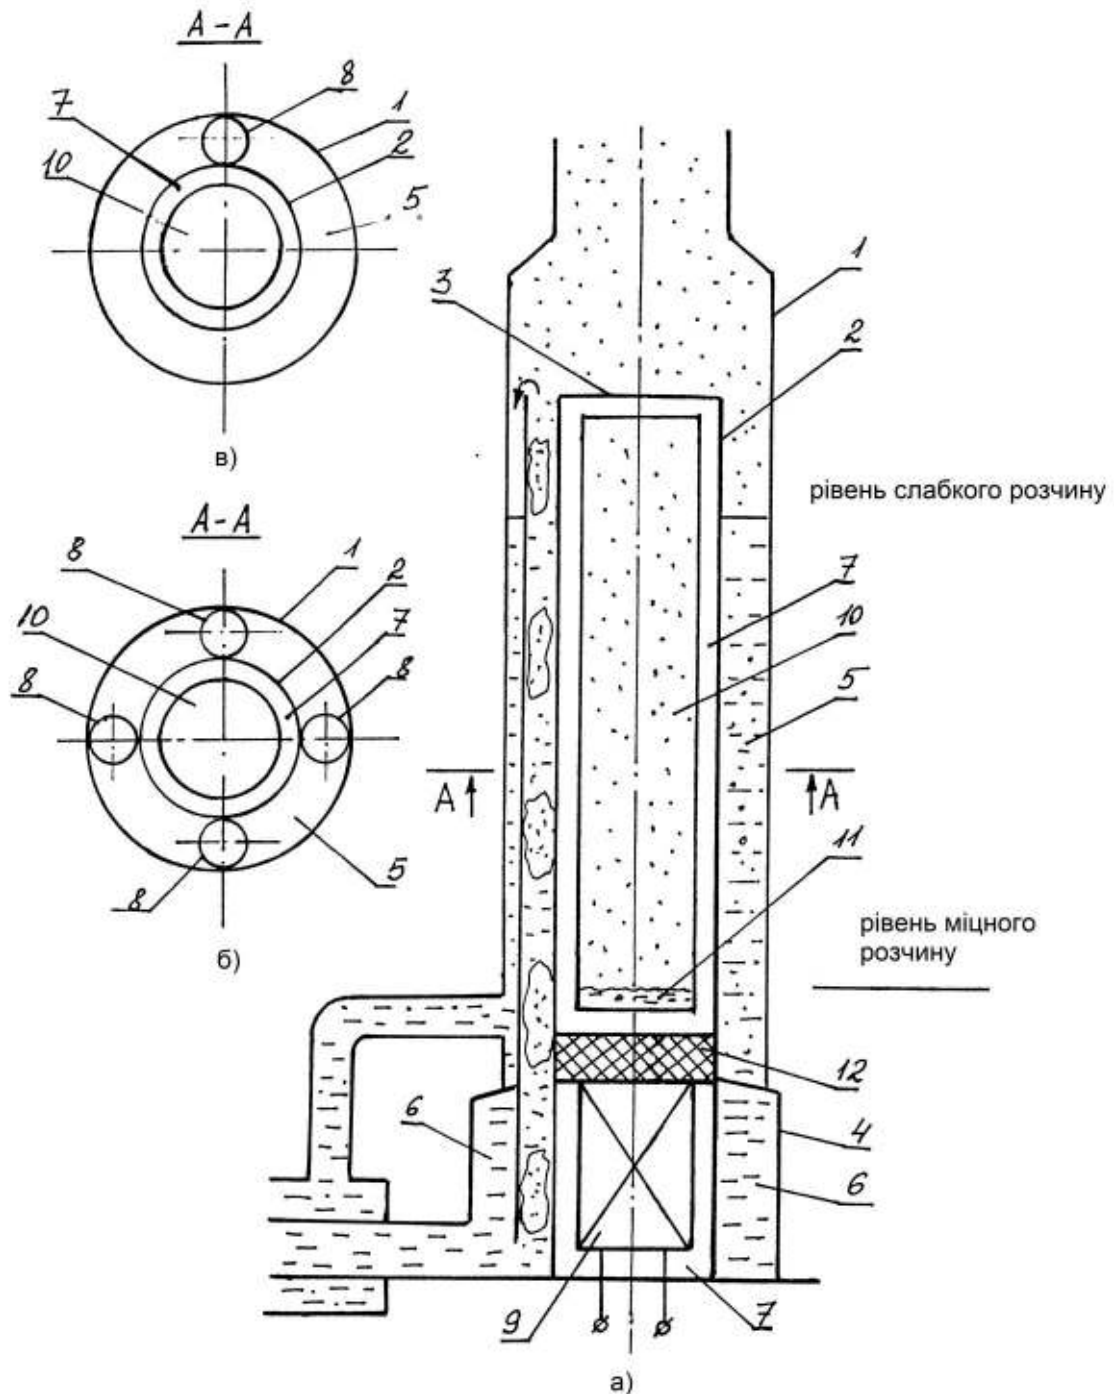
Конструкція генераторного вузла АХА з внутрішнім розташуванням джерела тепла: а) загальний вигляд; б) розріз А-А з одним генератором; б) розріз А-А з чотирма генераторами; 1 – корпус генератора; 2 – внутрішня порожнина; 3 – кришка внутрішньої порожнини; 4 – РТР; 5(б) – порожнина міцного (слабкого) ВАР; 7 – порожнина джерела теплового навантаження; 8 – генератор; 9 – джерело тепла; 10 – випарний-конденсаційний теплопередаючий пристрій; 11 – теплоносій теплопередаючого пристрою; 12 – теплоізоляція
